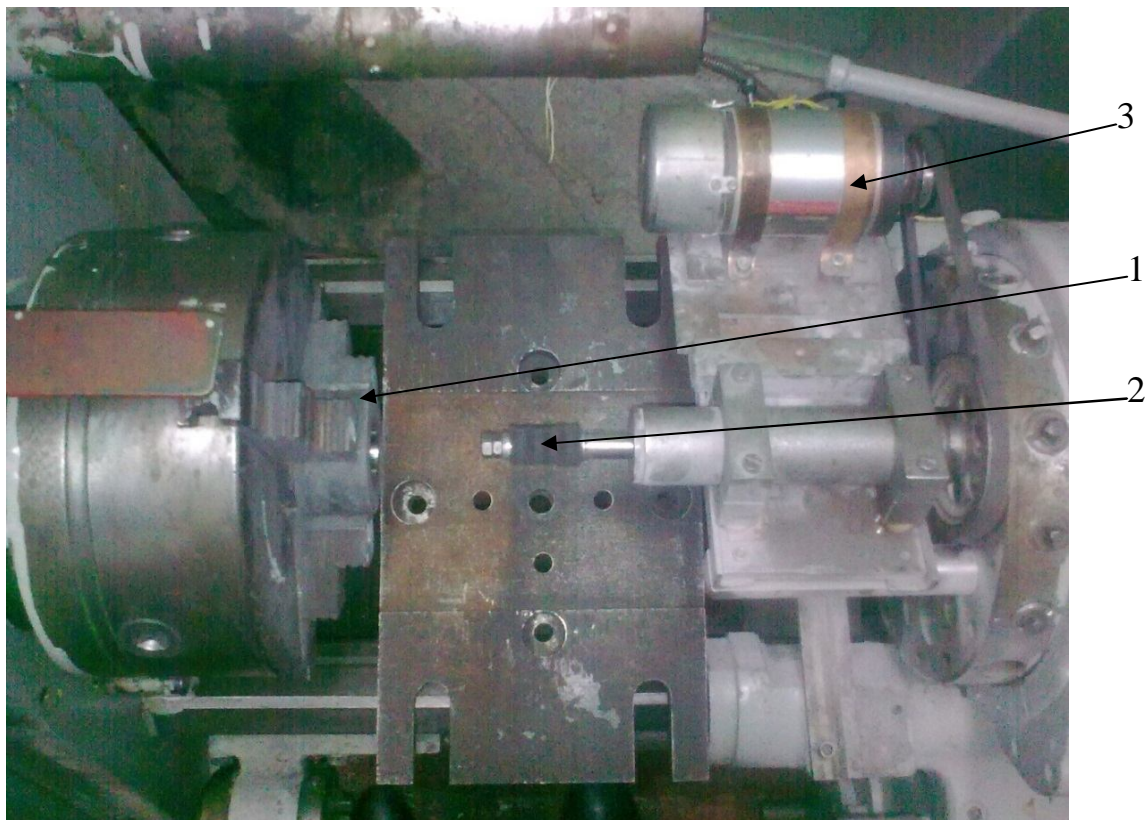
Вид сверху на экспериментальную установку для МАО внутренних поверхностей на базе токарно-револьверного станка 1341:
